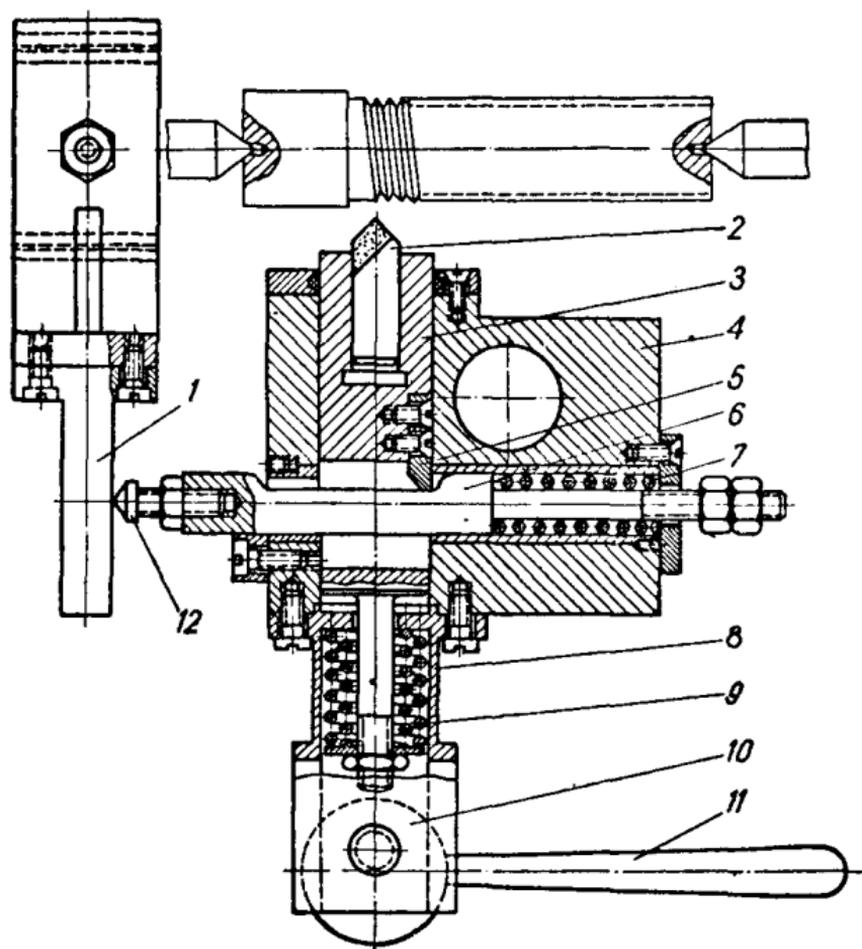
Приспособление для автоматического отвода резца при скоростном нарезании резьбы.
